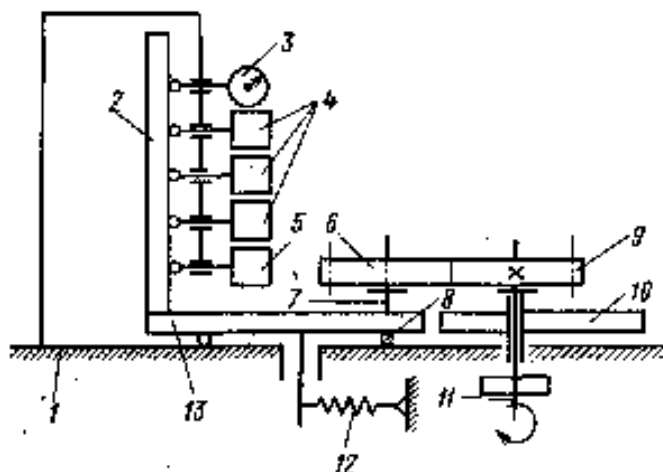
Схема автомата для контроля зубчатых колёс БВ-539К
